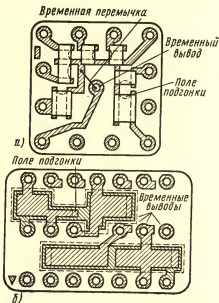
Платы с толстопленочными резисторами (а) и конденсаторами (б)
